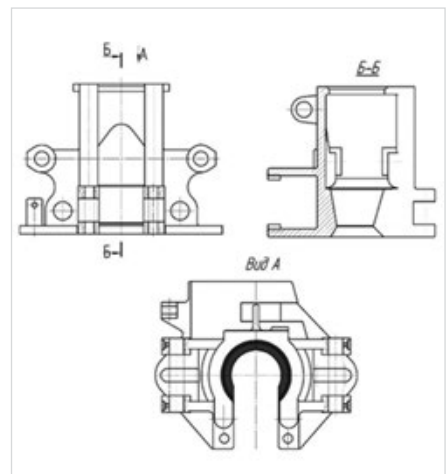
Общий вид корпуса спайдера СПГ-80 (заливкой обозначена изнашиваемая поверхность)
